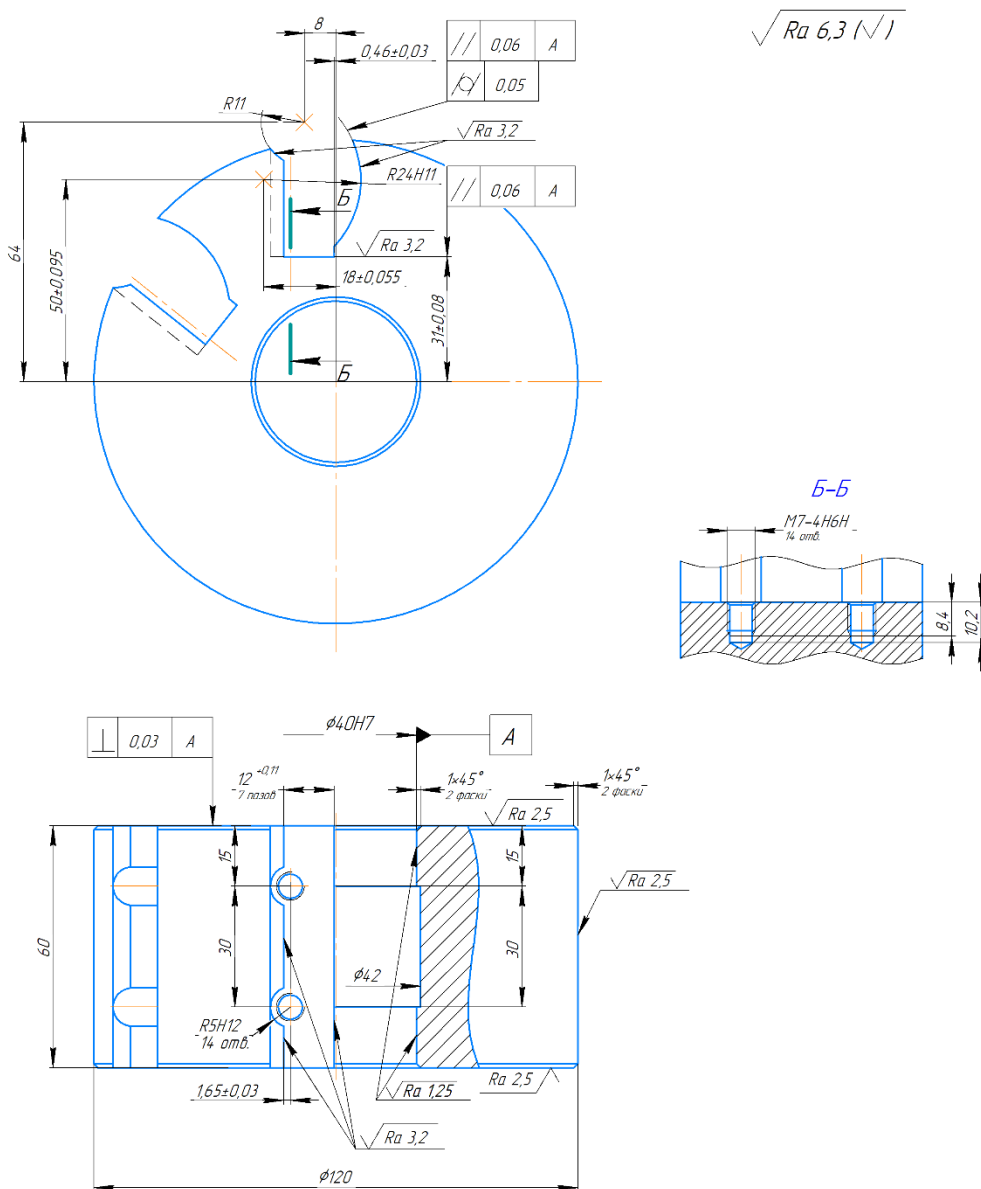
Чертеж корпуса дереворежущей цилиндрической сборной фрезы
